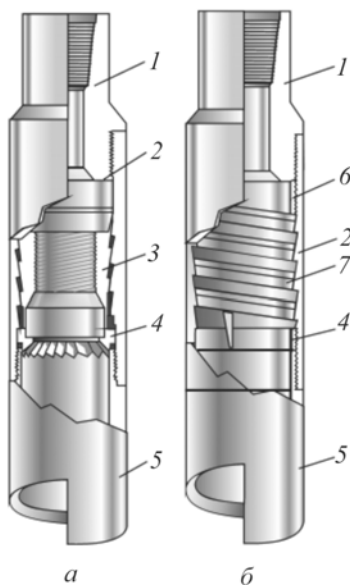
Овершот: *а* – с плащечным захватом; *б* – со спиральным захватом; 1 – верхний переводник; 2 – корпус; 3 – плащечный захват; 4 – ограничительное кольцо; 5 – направляющая воронка; 6 – пакер; 7 – спиральный захват
